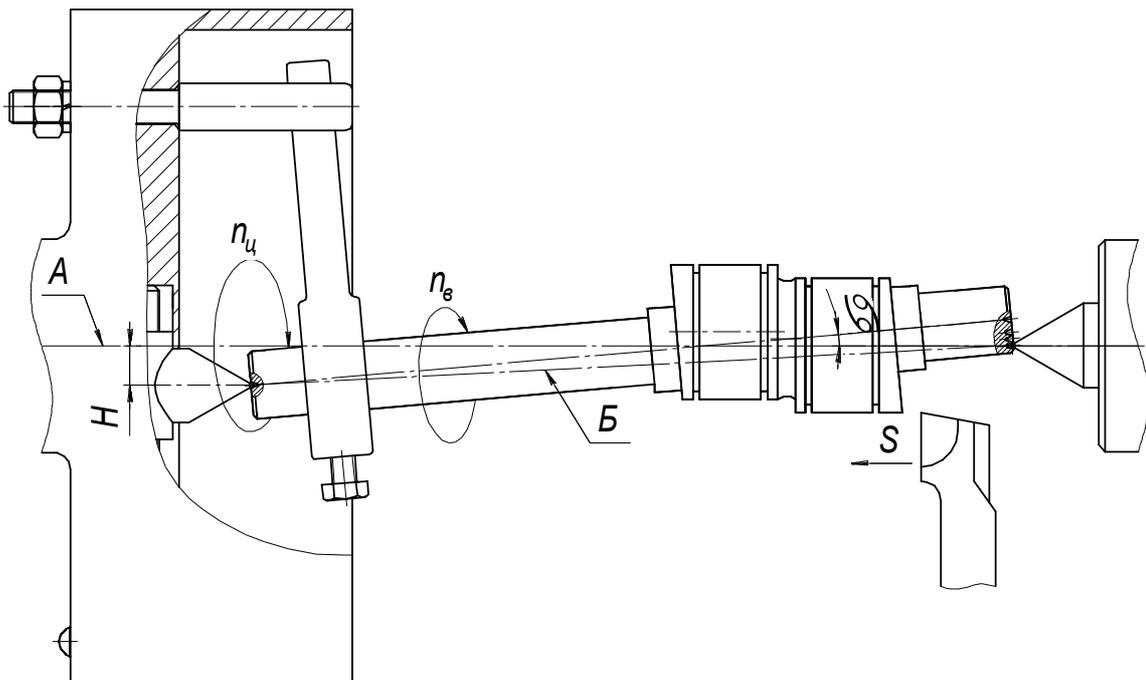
Схема обработки эксцентрикового вала ВППТК: n_u – частота вращения центра; n_e – частота вращения вала; S – подача режущего инструмента; H – величина смещения центрирующего элемента; α – угловой эксцентриситет; A – геометрическая ось станка; B – ось центров
